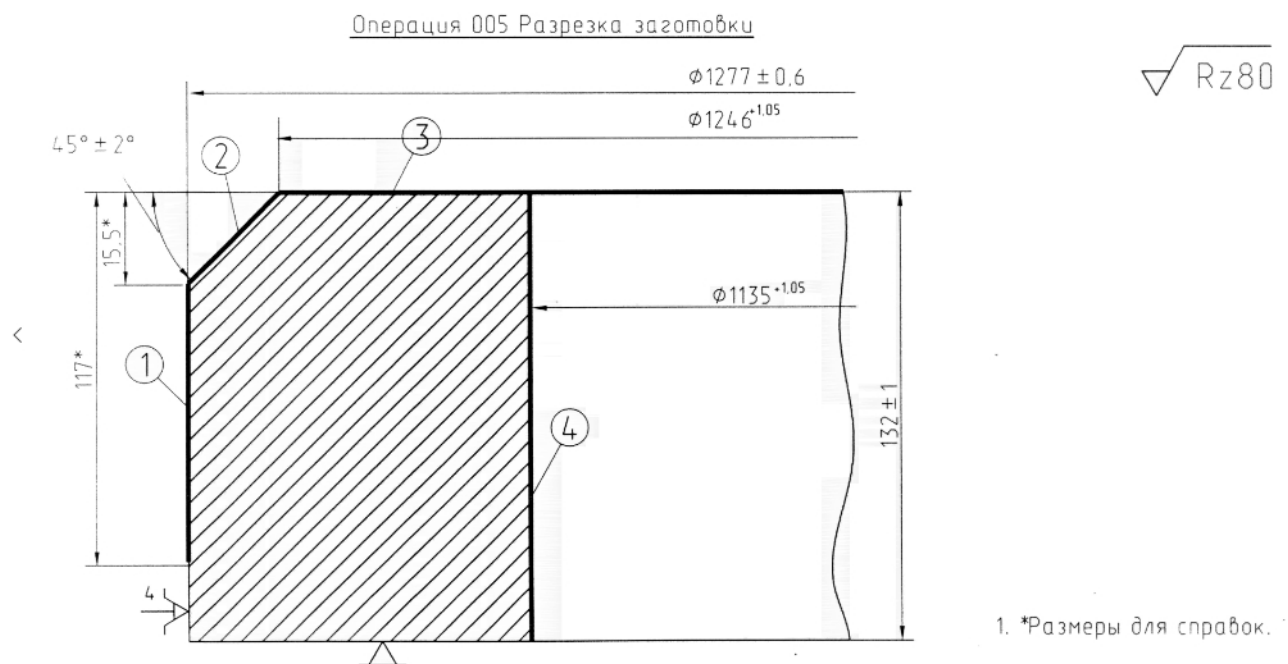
Токарно-карусельная операция 005 Разрезка заготовки
